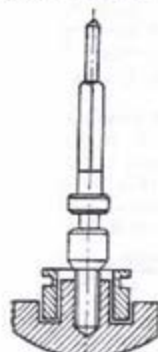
Axul remotor cu coroană și bucă de protecție.
